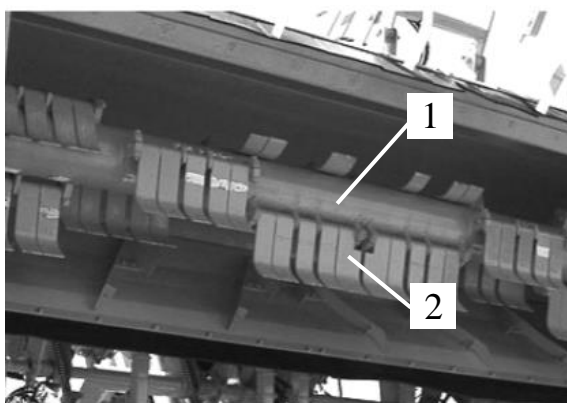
Загальний вигляд роторного гичкоріза: 1 – барабан; 2 – ніж
